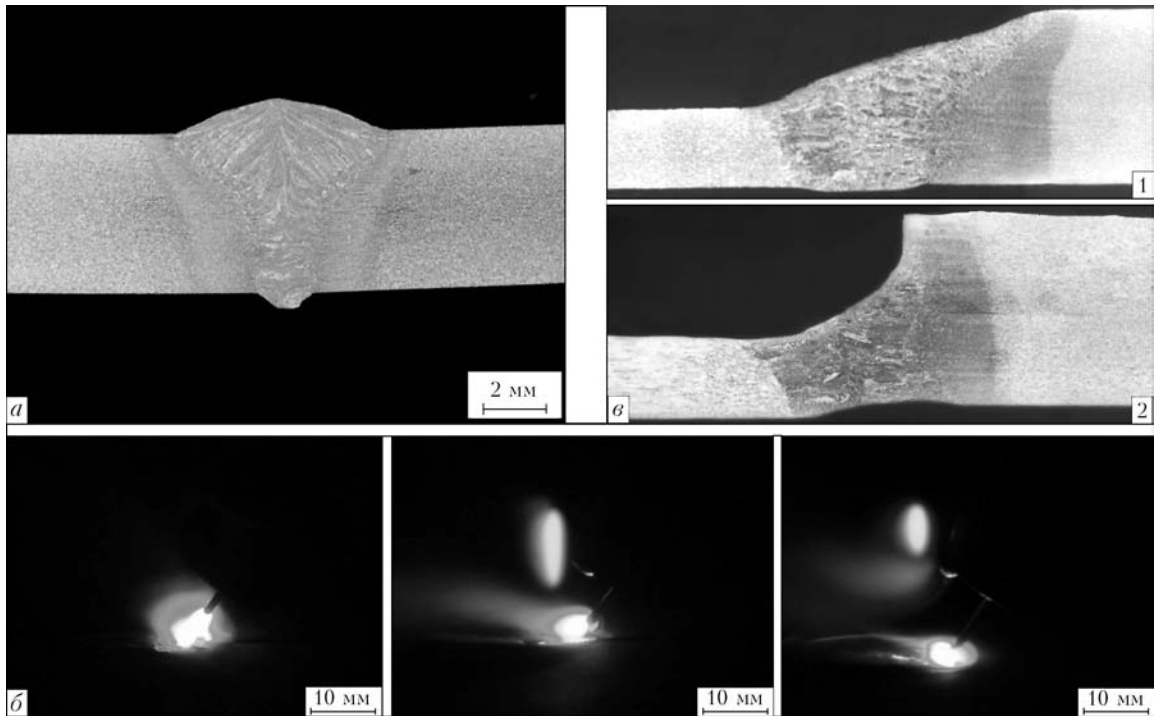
Гибридная сварка CO₂-лазером + МИГ (а) и стабильная гибридная сварка CO₂-лазером + МИГ/МАГ с различными защитными газами (б) соответственно при частичной и полной блокировке лазерного пучка с помощью оторванного плазменного облака; в — гибридная сварка CO₂-лазером + ТИГ (обозначения 1, 2 см. в тексте)
